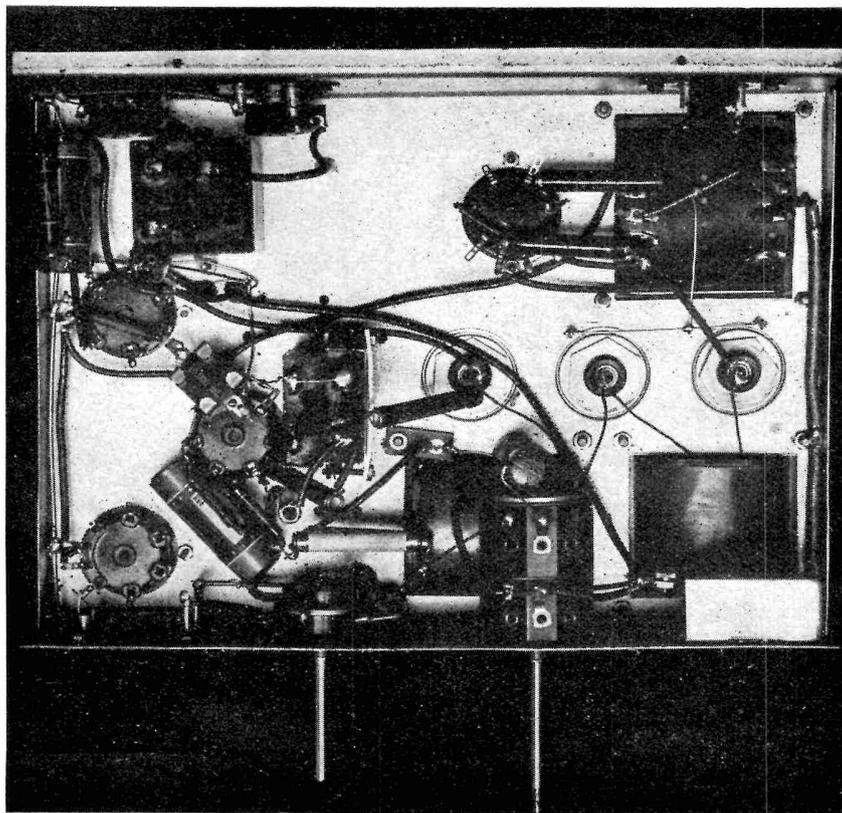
Photographie du châssis de l'ampli vu de dessous.
